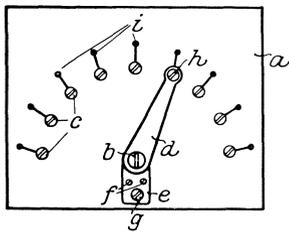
Kontaktplatte, z. B. für eine Stufenspule.
